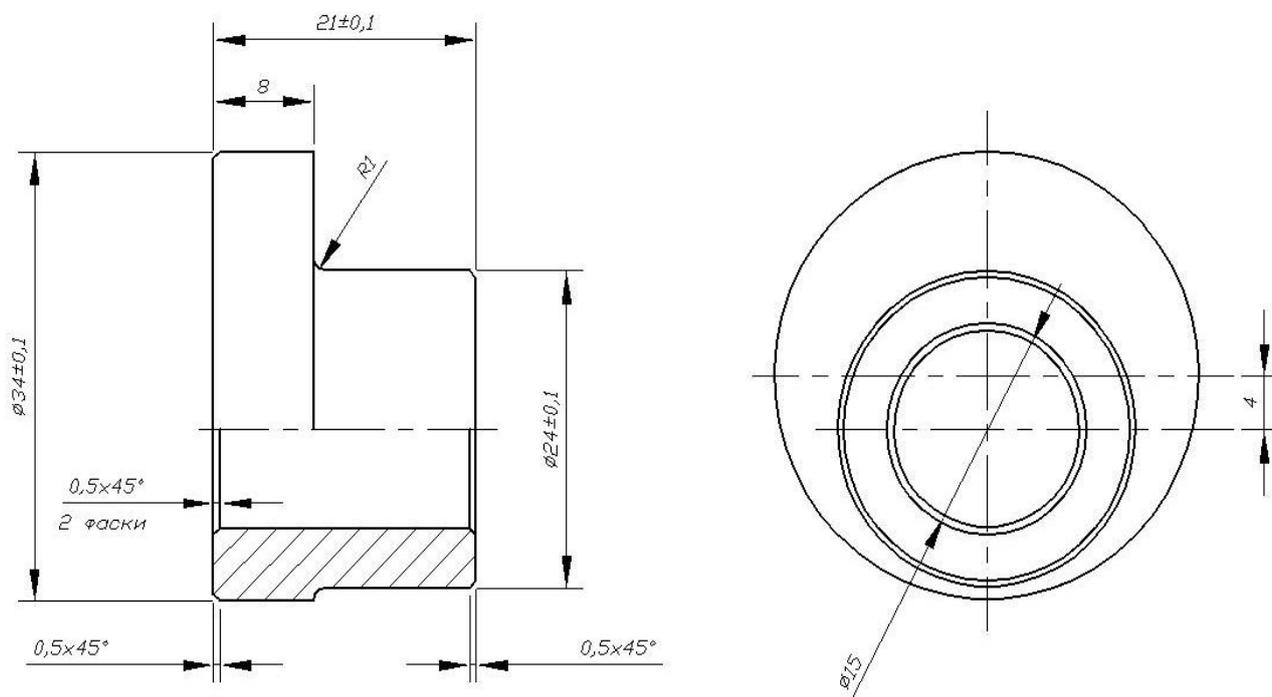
Чертеж детали «эксцентрик» для насоса высокого давления дизельного двигателя
